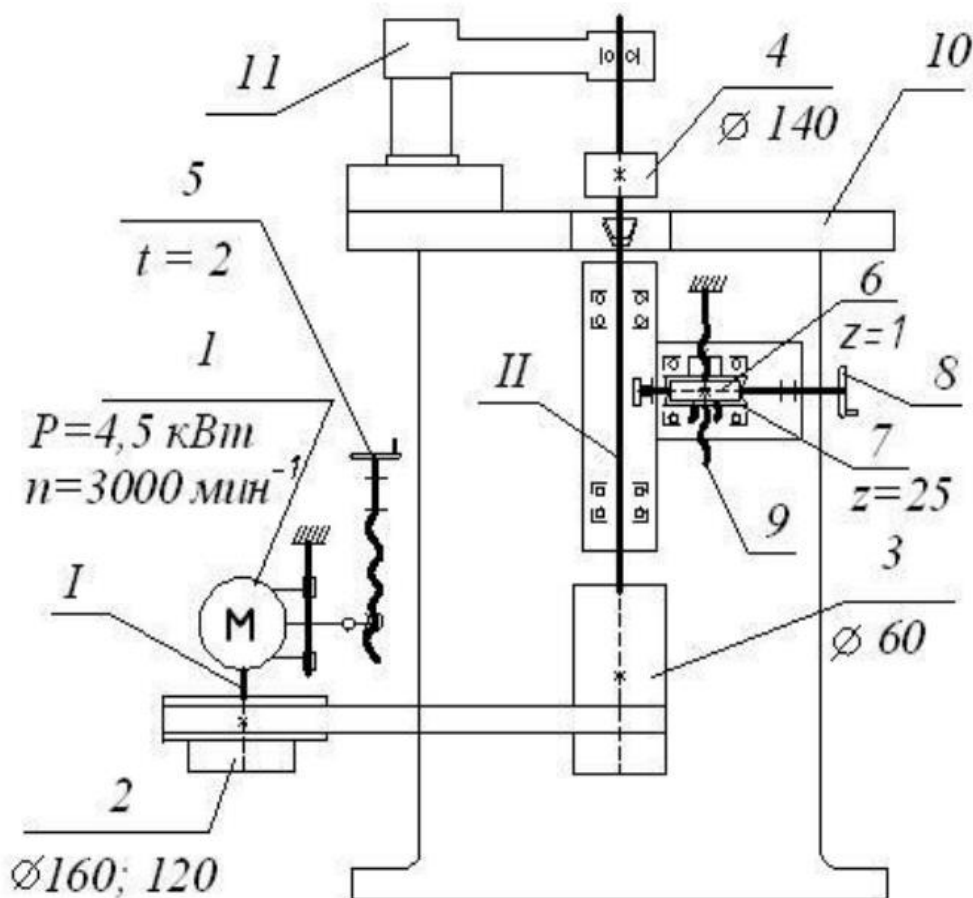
Кинематическая схема фрезерного станка Ф4
